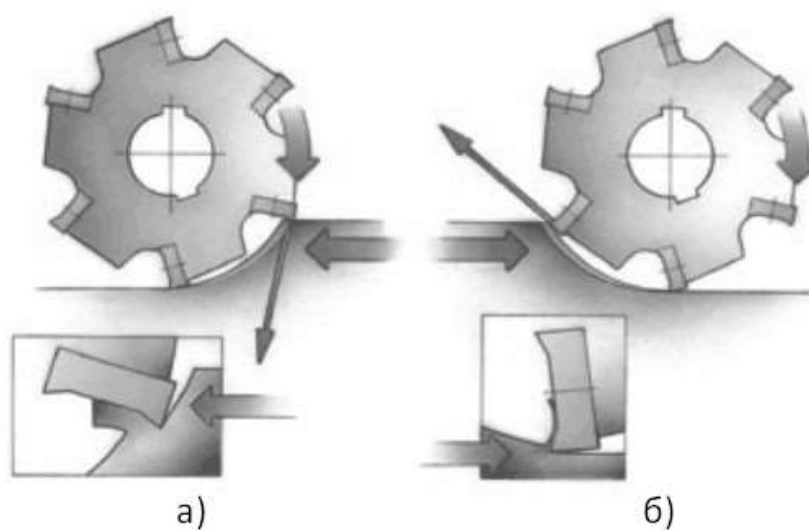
Напрямки фрезерування (а – попутне, б – зустрічне)
